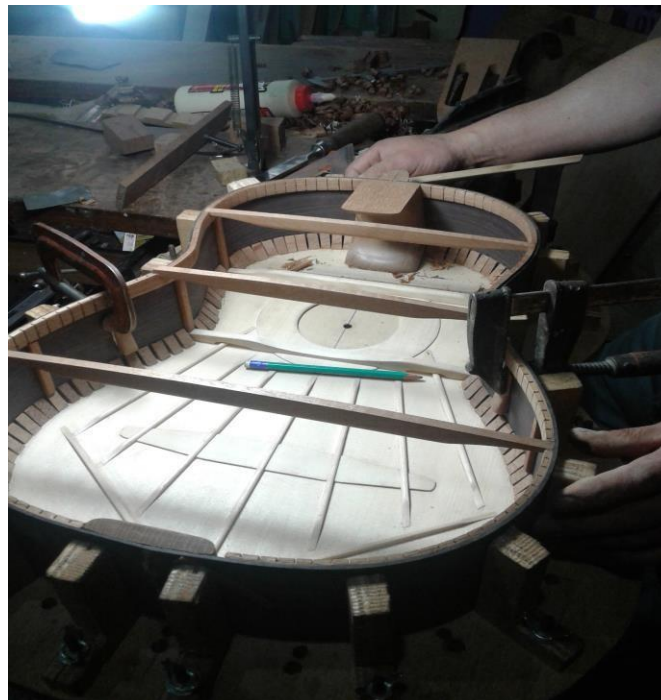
Colocación de las barras armónicas. Fotografía Carlos Calle.
